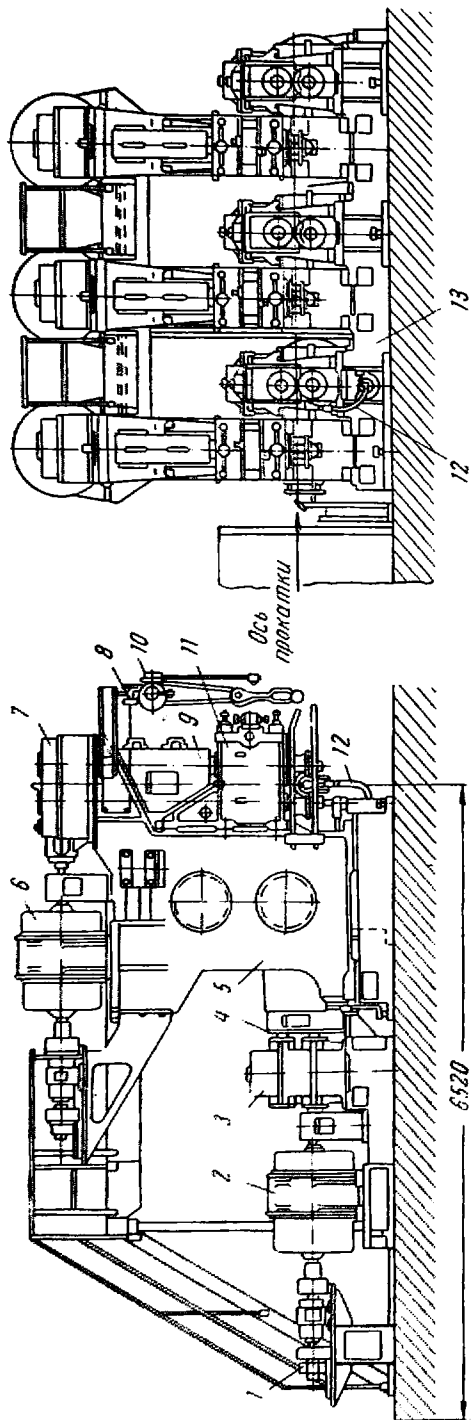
Формовочно-сварочный стан с индивидуальным приводом
